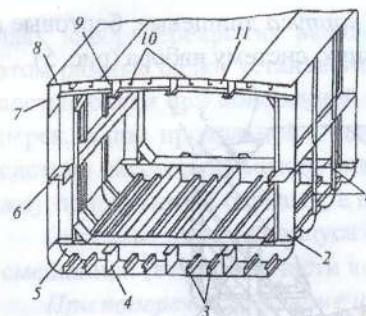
Конструкция корпуса со смешанной системой набора:
